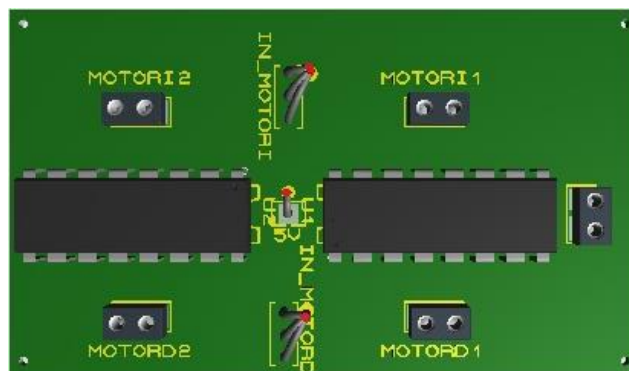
Placa PCB en 3D del Circuito de potencia a motores
